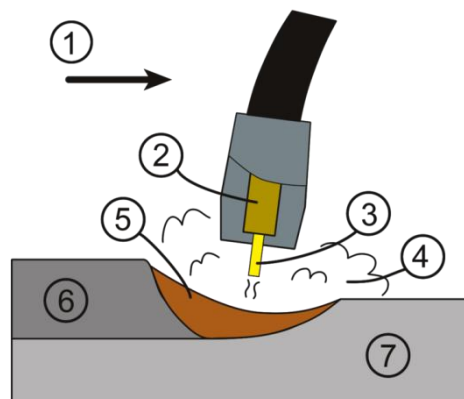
Detalle del proceso de soldadura MAG. Fotografía obtenida de la web Wikipedia.org 1. Dirección de la soldadura 2. Tubo de contacto 3. Hilo 4. Atmósfera de gas protector 5. Baño de fusión 6. Cordón de soldadura 7. Metal de base.
